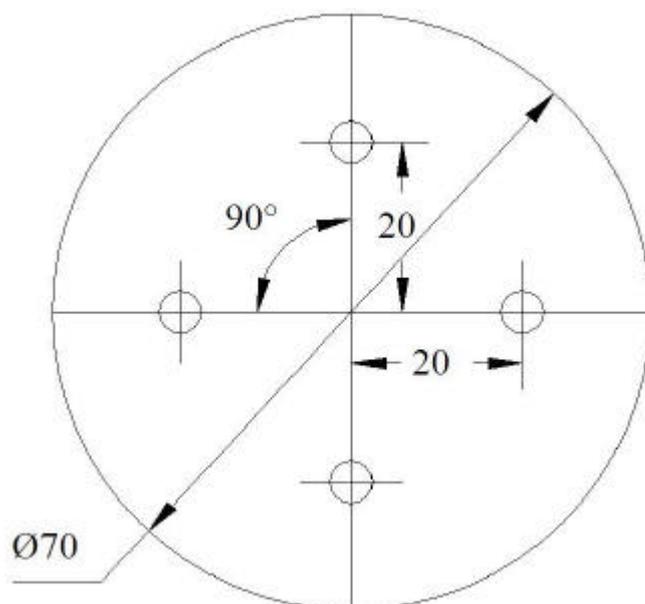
posizione dei tacchetti (centri) sul piede di prova (dimensioni in mm)
